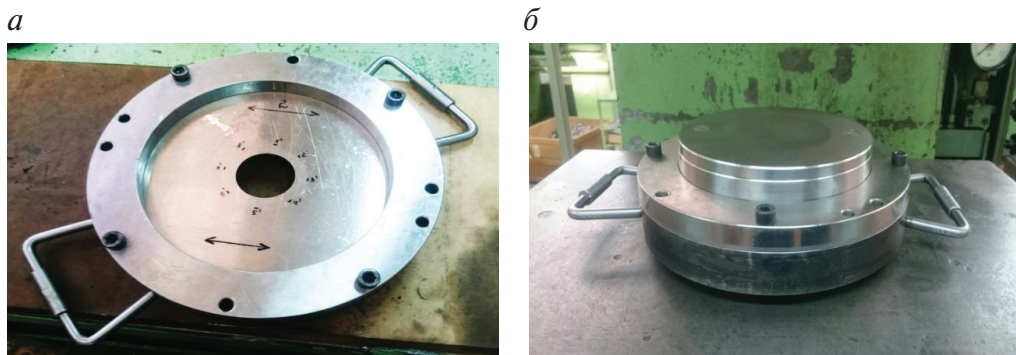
Листовая заготовка с разметкой между матрицей и прижимом (а) и штамп в сборе (б)
